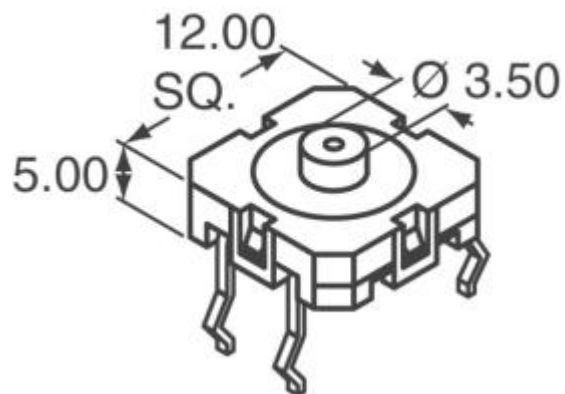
Габаритный чертёж кнопки «Racon12»
